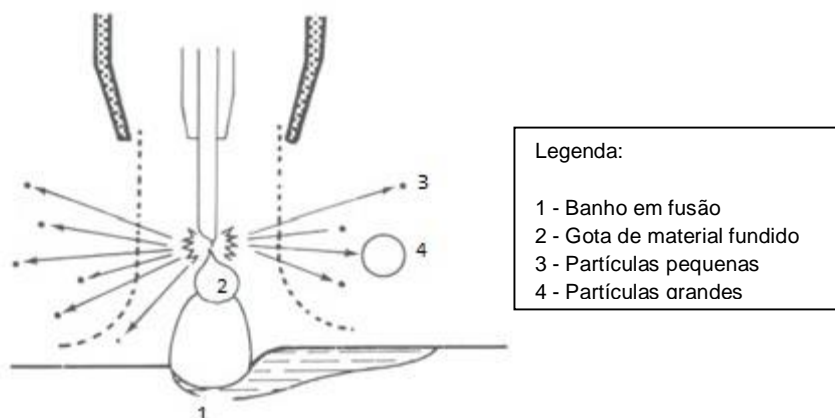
Elementos do processo de soldadura e de transferência de metal que geram fumos [20]
